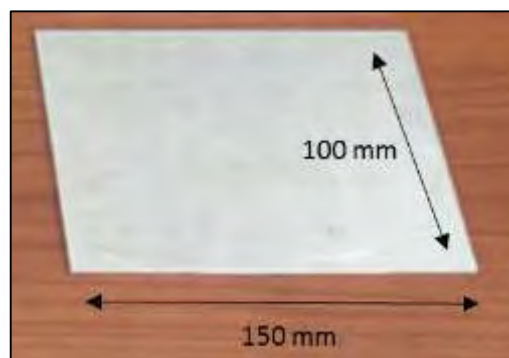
Plancha de aluminio AA6063 para la fabricación de cupones de soldadura.
